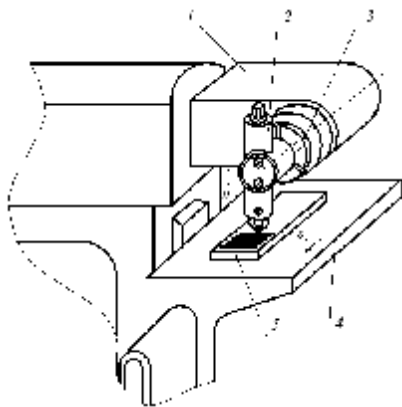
Схема пристрою для утворення канавок із змінною глибиною: 1 – шпиндель; 2 – накатний інструмент; 3 – цанговий патрон; 4 – стій; 5 – деталь, яка оброблюється
